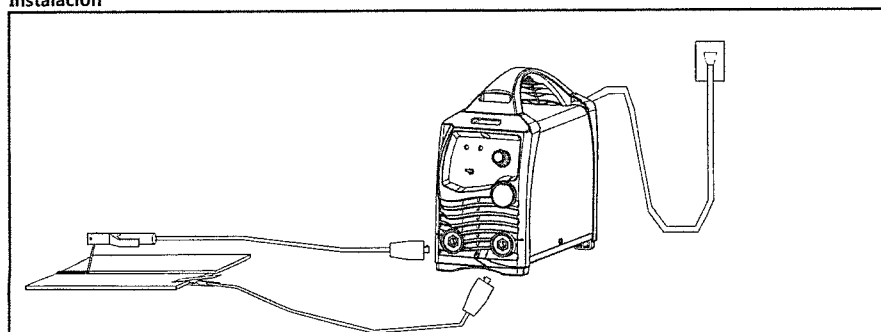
Diagrama esquemático de Soldadura MMA
